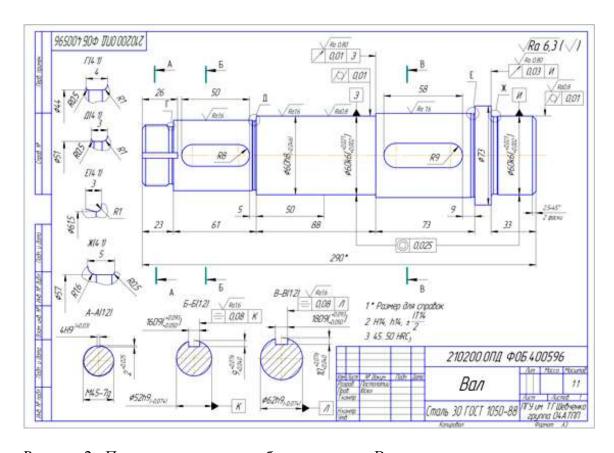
Пример выполнения рабочего чертежа Вал
